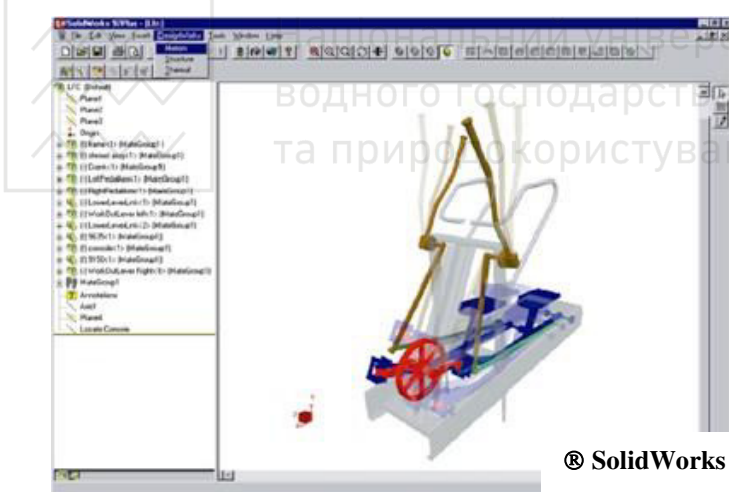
Робоче вікно системи інженерних розрахунків конструкцій DesignSpace для SolidWorks
